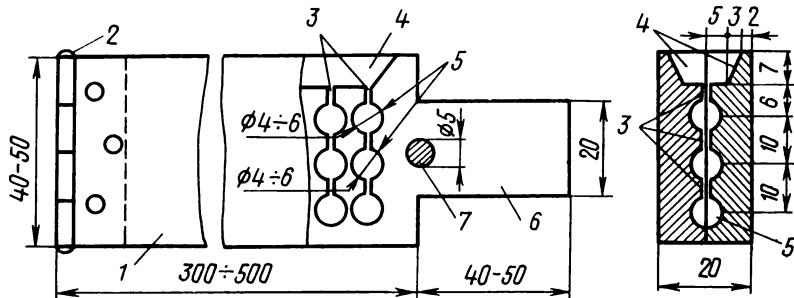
Форма для отливки крупных номеров дроби и картечи:
